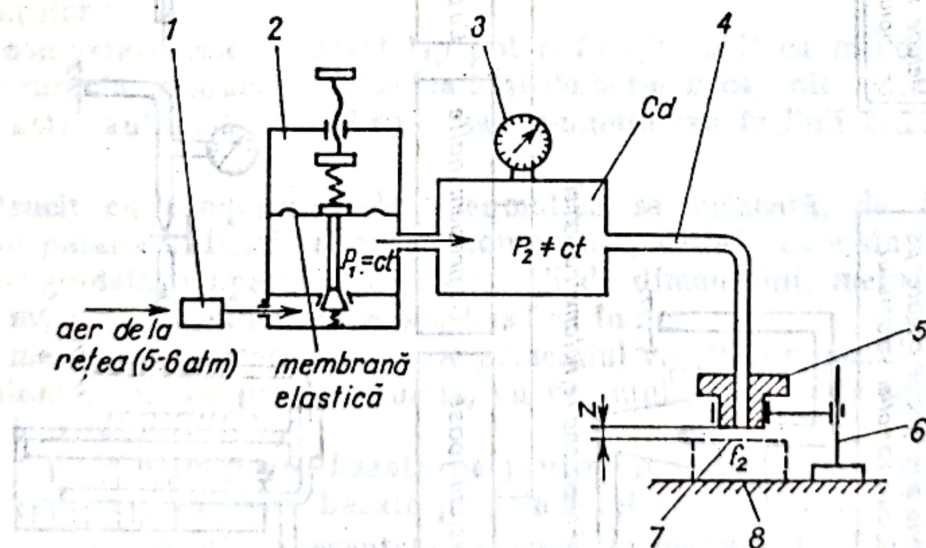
Instalație pneumatică de măsurare a dimensiunilor.
